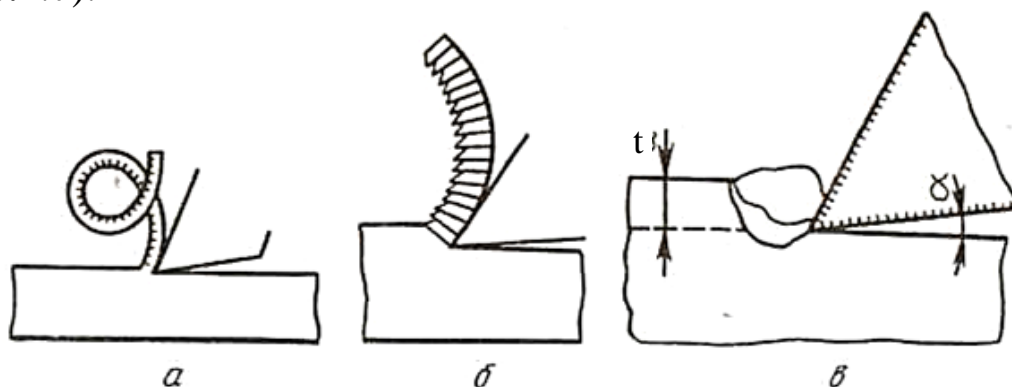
Виды стружек: а – сливная; б – скалывания; в - надлома
